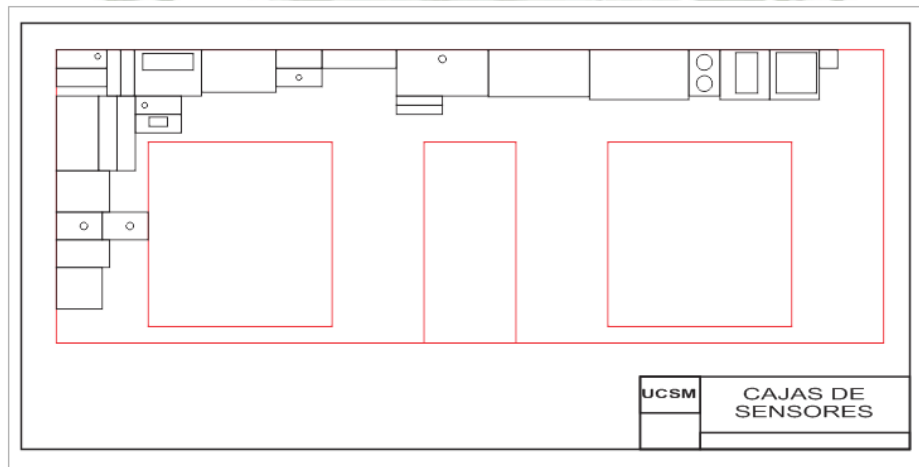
Distribución de las piezas en la plancha a comprar
